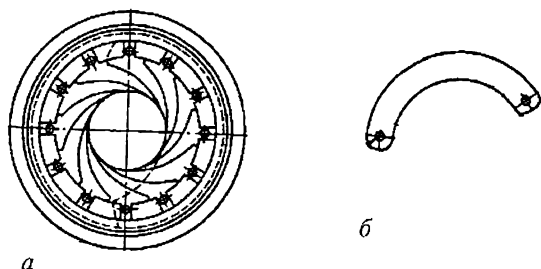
Ирисовая диафрагма: а) внешний вид ирисовой диафрагмы; б) непрозрачная дугообразная (серпообразная) пластинка (лепесток).
